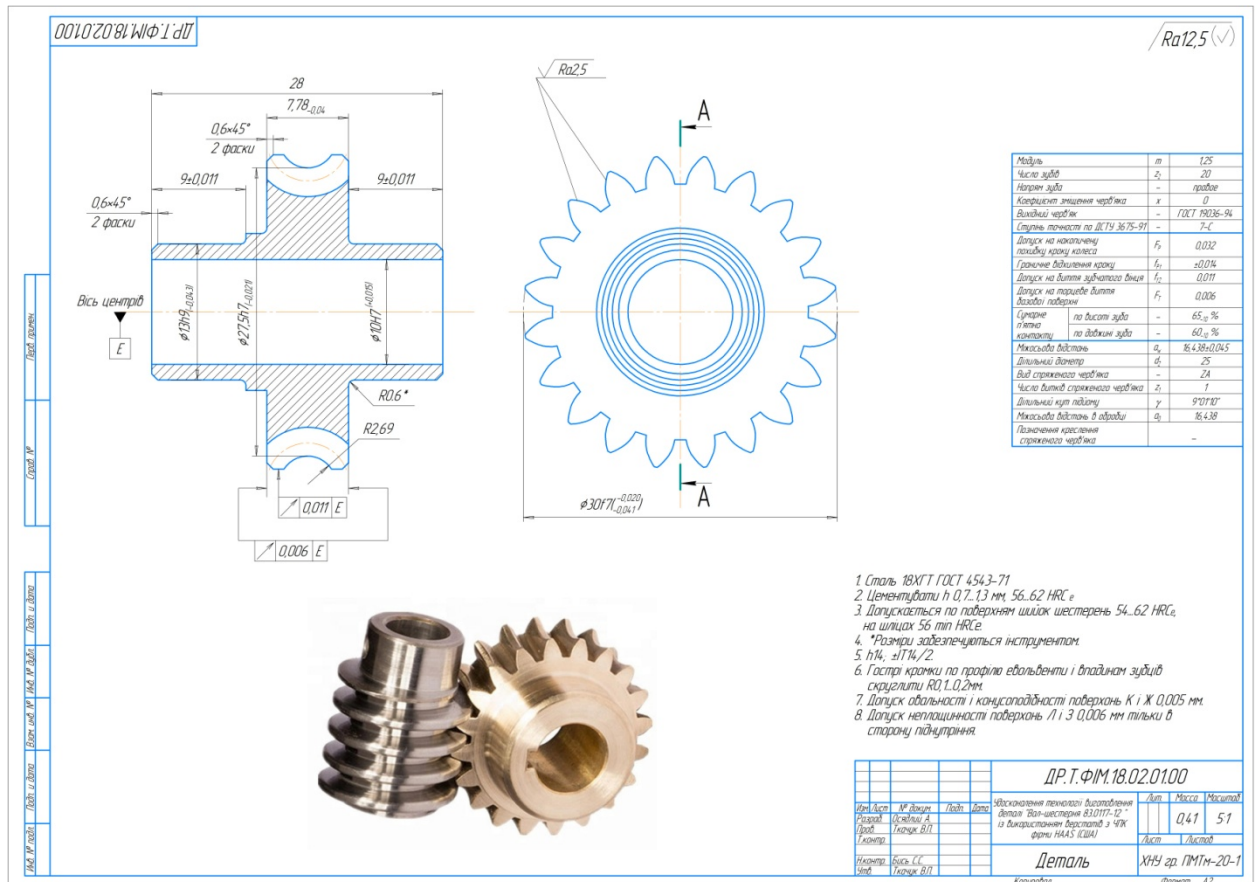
Креслення деталі черв'ячне колесо
